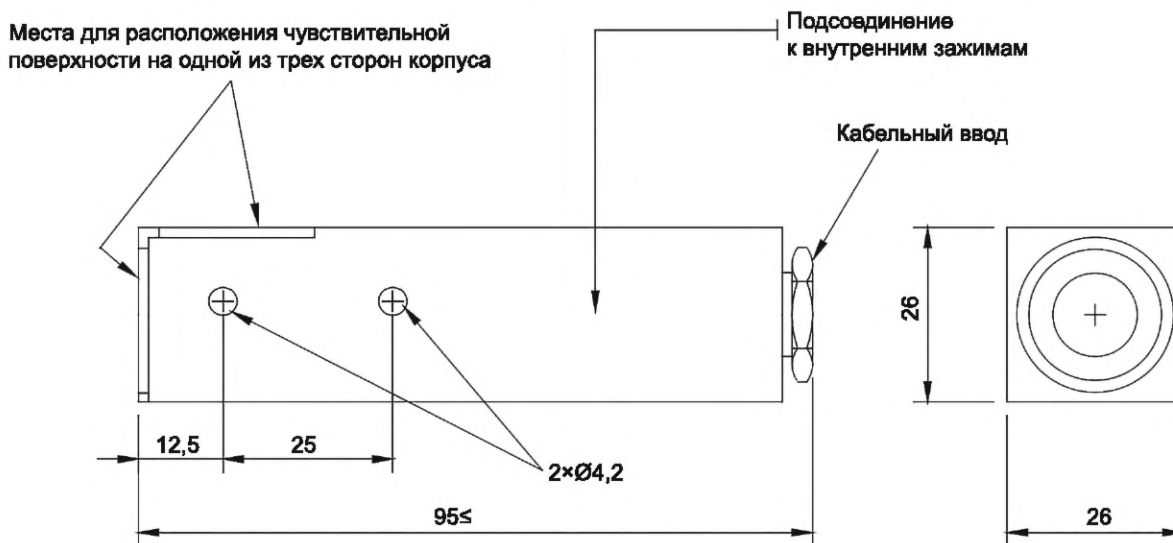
Габаритные размеры сенсорного выключателя типа I1C26
